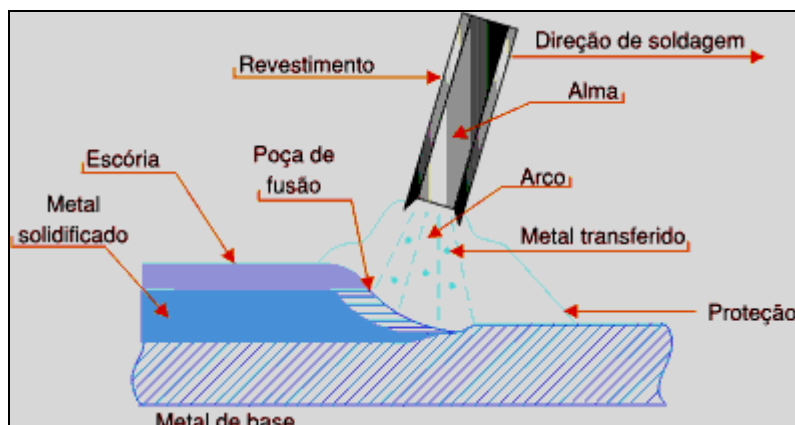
Esquema do processo de soldagem por Eletrodo Revestido.
